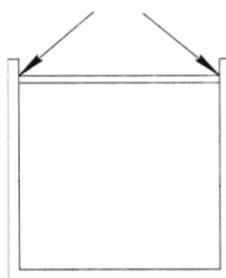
Схема сварки угловых продольных швов двухдуговым автоматом
